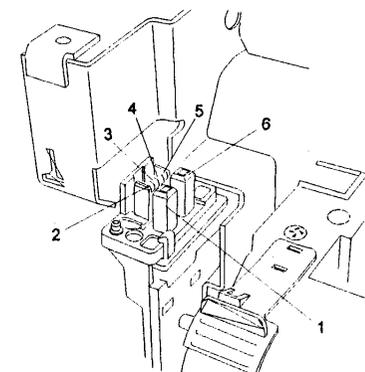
Разъем модуля фюзера, закрепленный на корпусе аппарата
